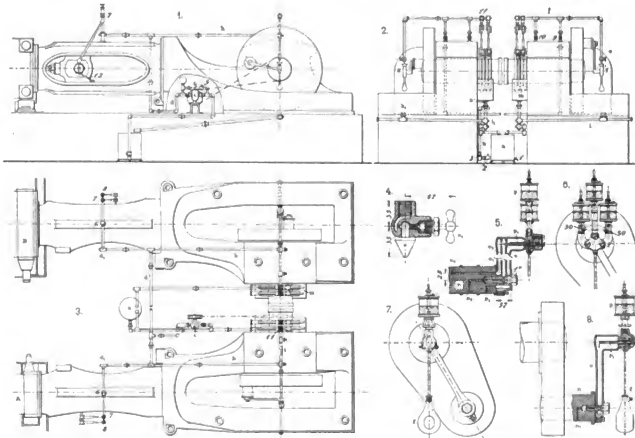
Z. A.: Zentralschmierung für Maschinenaggregate.
